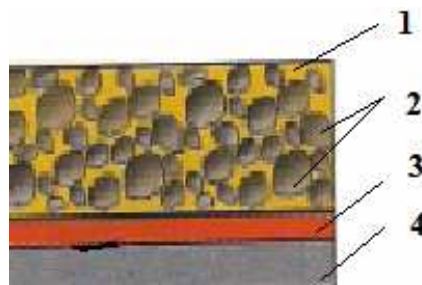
Металлофторопластовый подшипник из ленты, полученный методом порошковой металлургии
